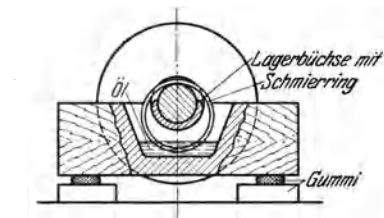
Lagerung eines Läufers mit einteiliger Lagerbüchse auf einer Hartholzunterlage.
